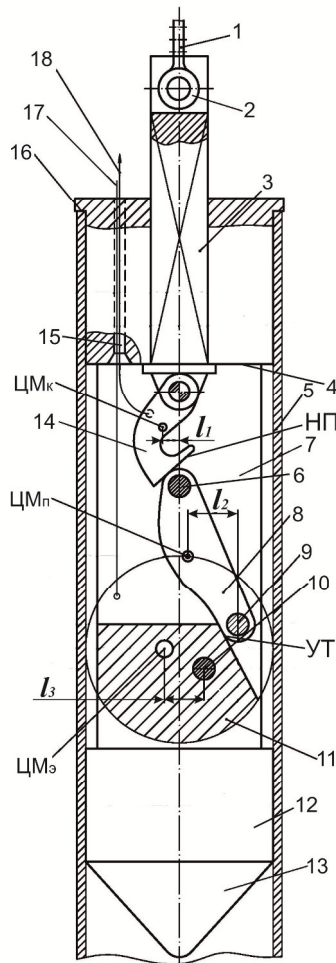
Полуавтоматический эксцентриковый захват трубы: 1 – канат, 2 – ось устройства подвеса, 3 – ползун прямоугольного сечения, 4 – упорный торец ходового цилиндра, 5 – труба, 6 – ось проушины верхняя, 7 – паз П для размещения в нём крюка, проушины и эксцентрика, 8 – проушина, 9 – ось проушины нижняя, 10 – ось эксцентрика, 11 – эксцентрик, 12 – корпус ходового цилиндра, 13 – конус направляющий, 14 – крюк, 15 – отверстие для прохода канатов, 16 – посадочный торец, 17 – канат поворота эксцентрика, 18 – канат поворота крюка, ЦМ_к – центр масс крюка, ЦМ_п – центр масс проушины, ЦМ_э – центр масс эксцентрика, НП – направляющая поверхность, УТ – упорный торец для проушины
